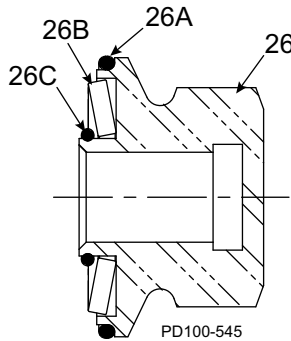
Querschnittsansicht der Rotormutterbaugruppe, wie montiert
